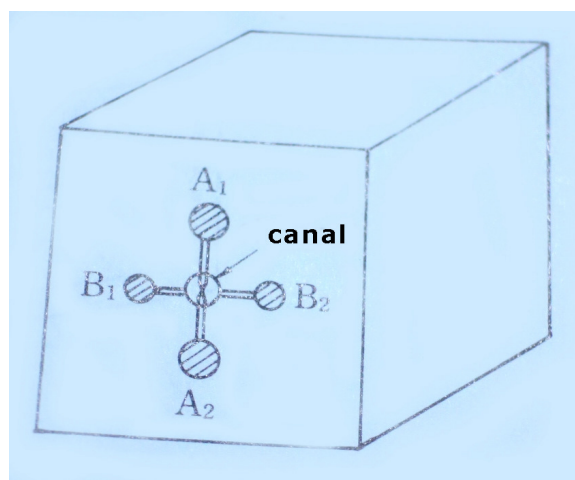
Mudança de molde “One-Touch”, adaptado Shingo (1985)
